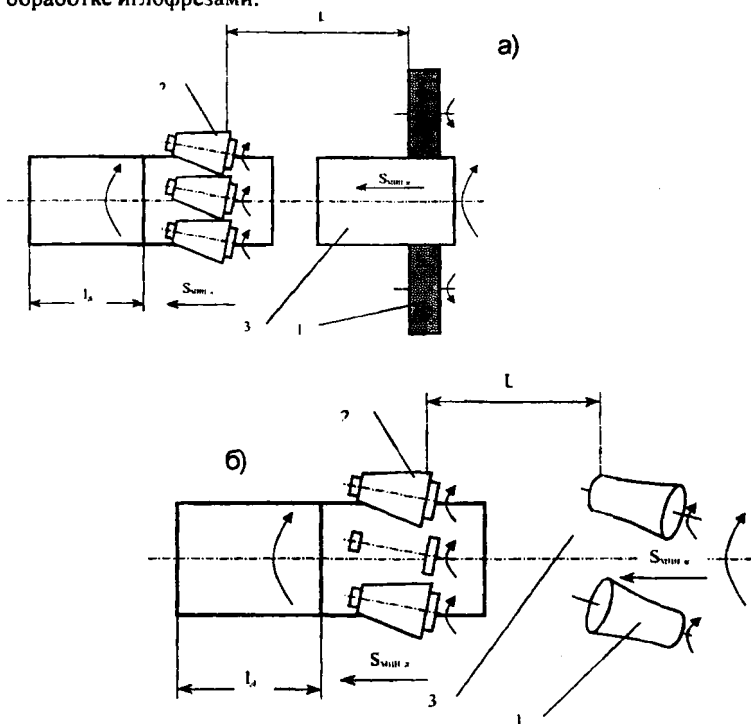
Схема реализации способа комбинированной обработки иглофрезерованием и ППД: (1 – иглофреза, 2 – деформирующий элемент, 3 – обрабатываемая заготовка): а – с принудительной подачей при обработке иглофрезами; б – с самоподачей при обработке иглофрезами
